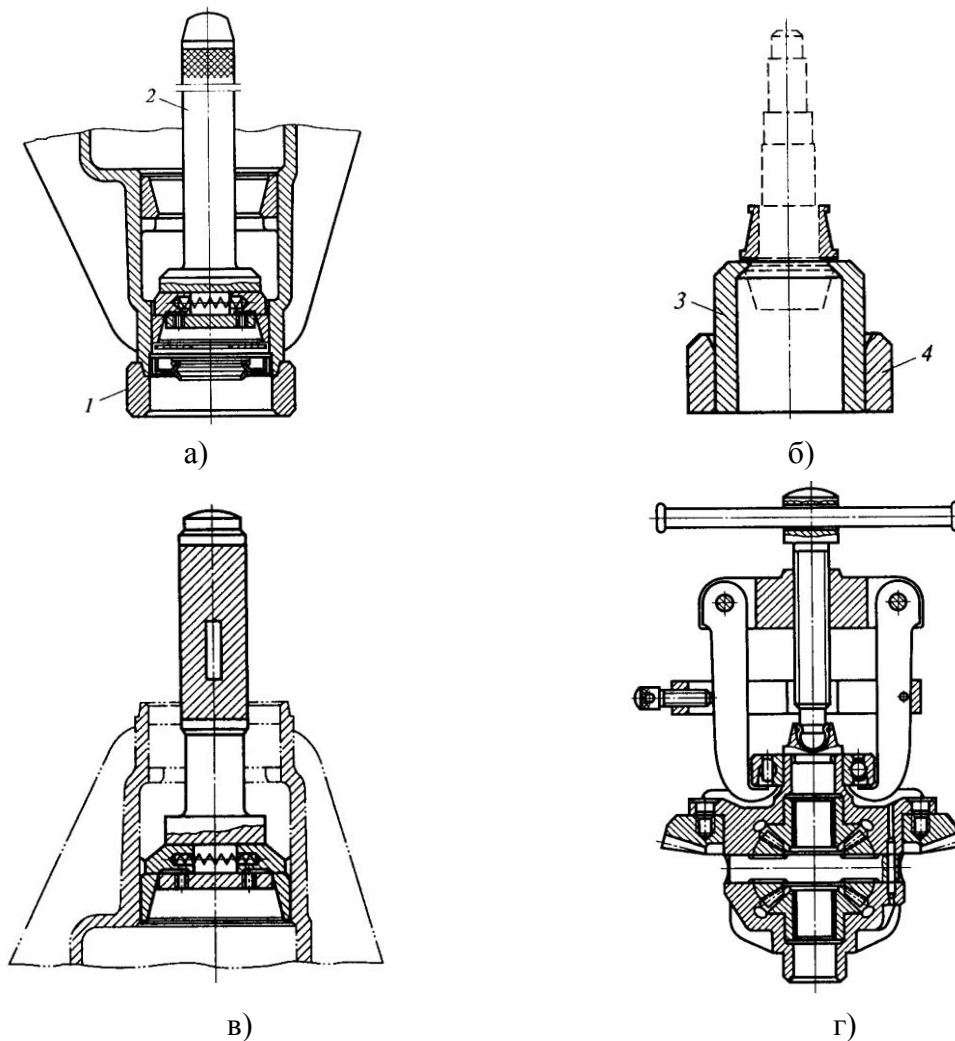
Приспособления для разборки редуктора заднего моста автомобилей Москвич-412, - 2140:
